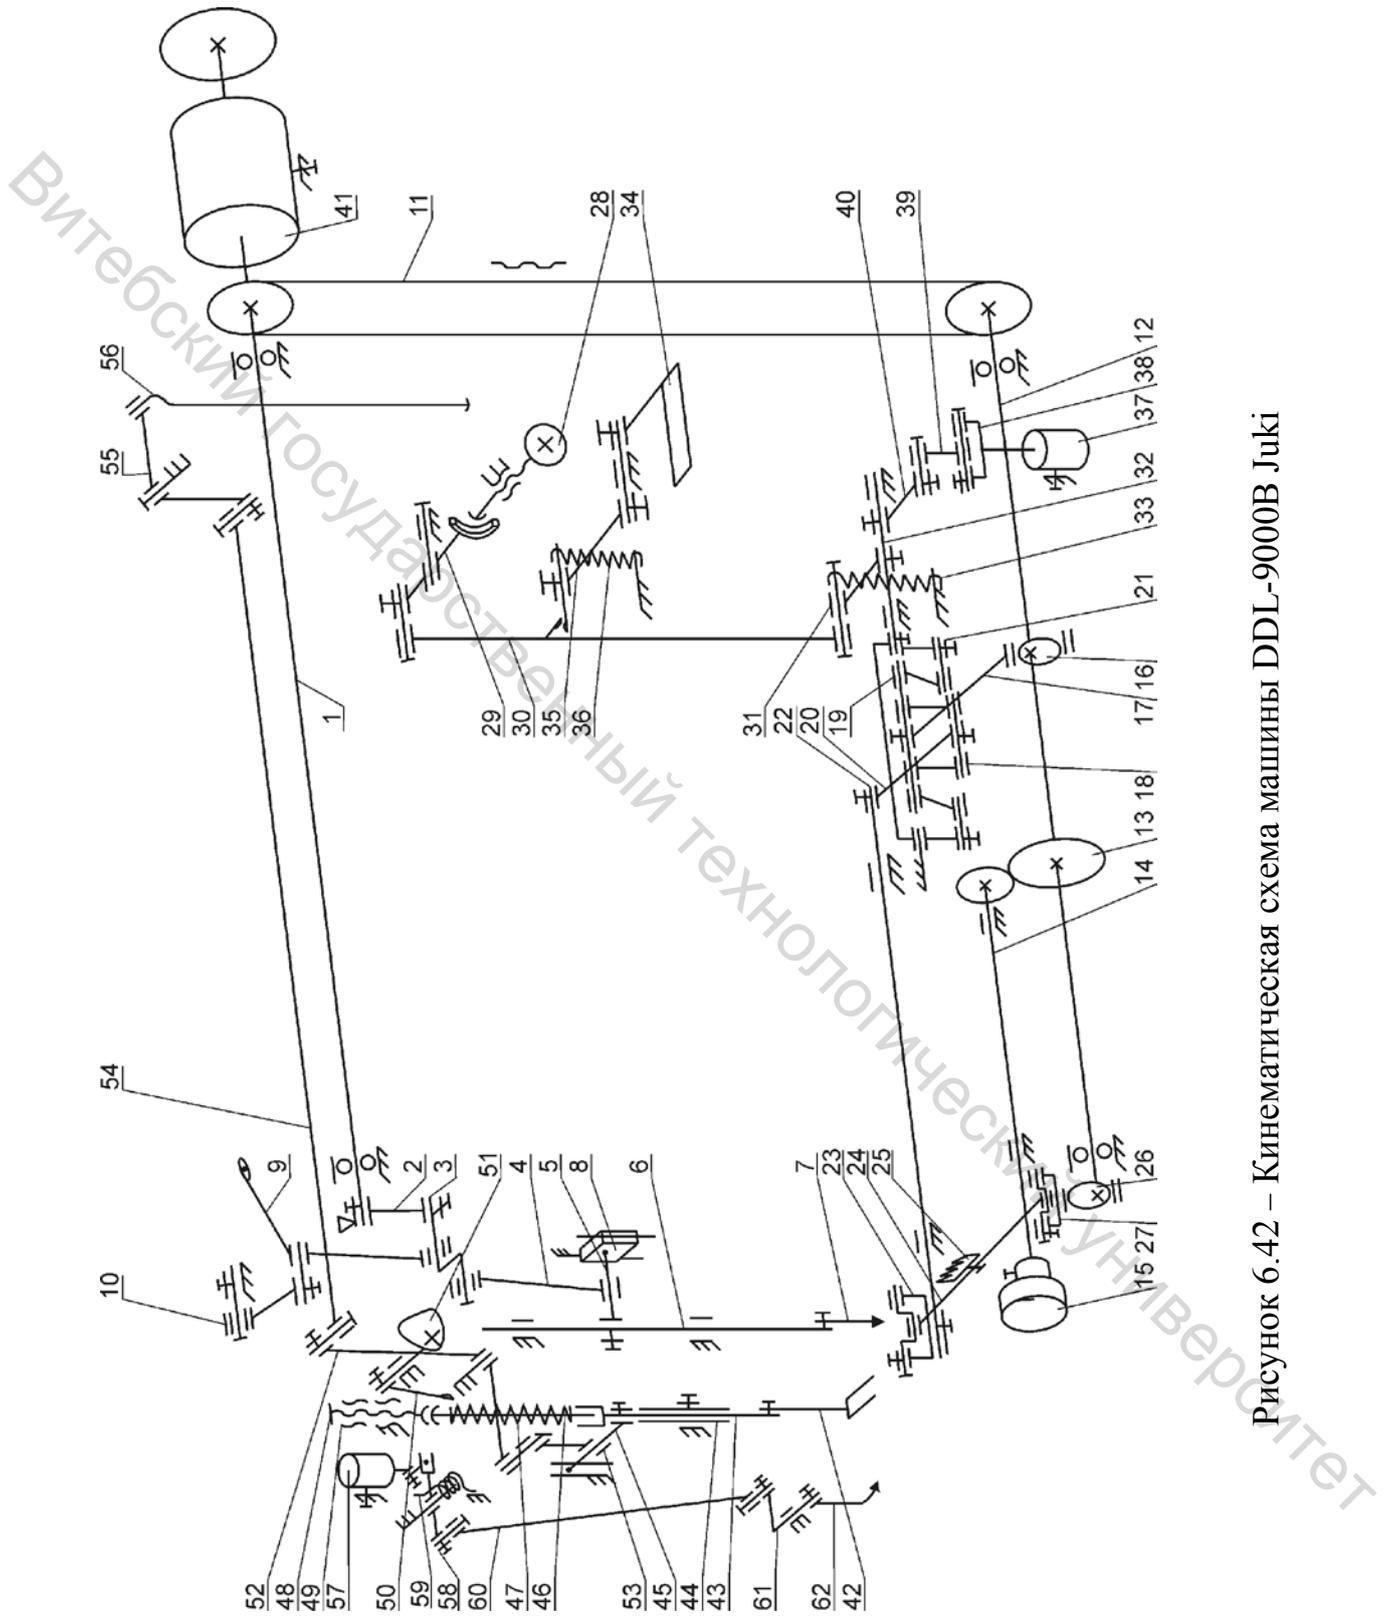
Кинематическая схема машины DDL-9000B Јуќи
